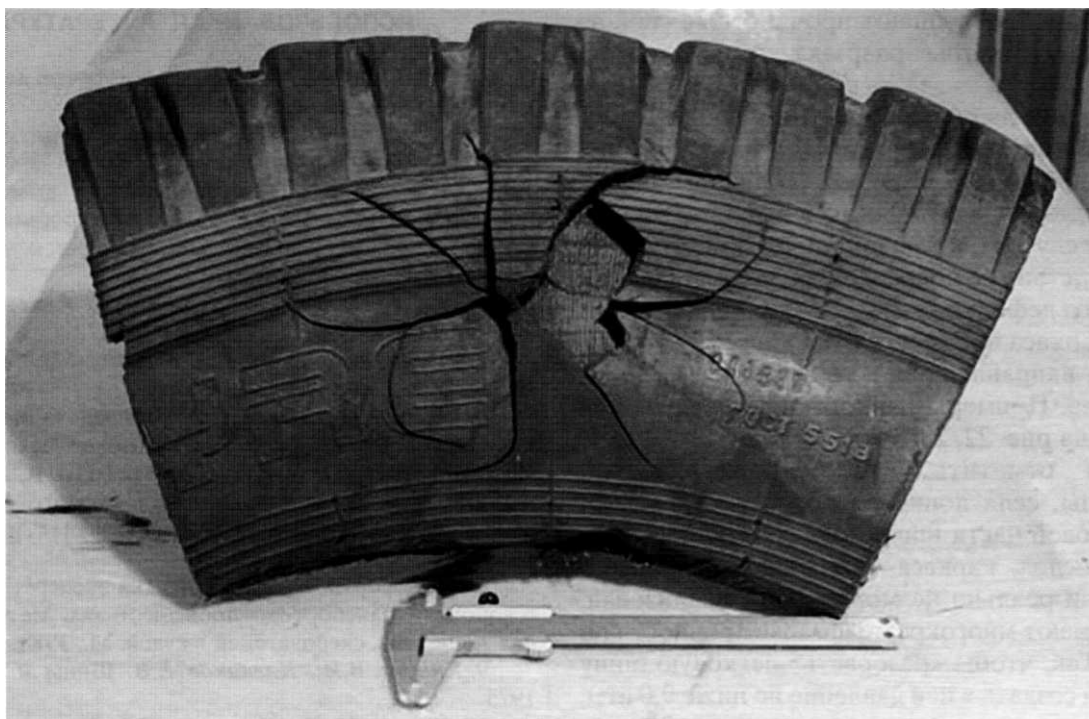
Разрушение, имеющее вид «пневматического взрыва» камерной шины
